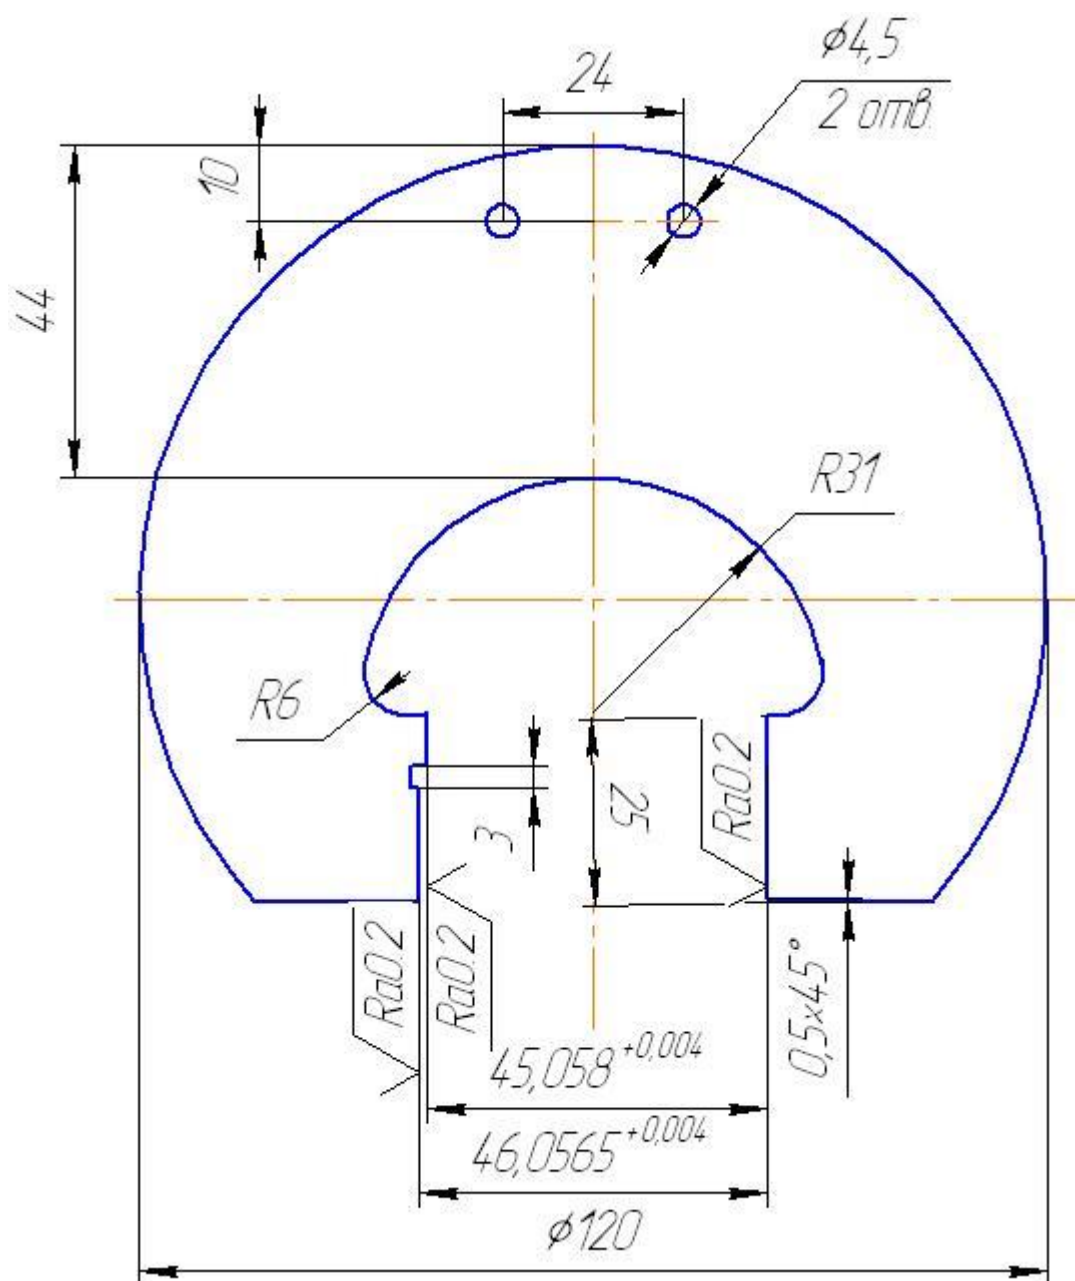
Пример обозначения исполнительных размеров калибра-скобы
